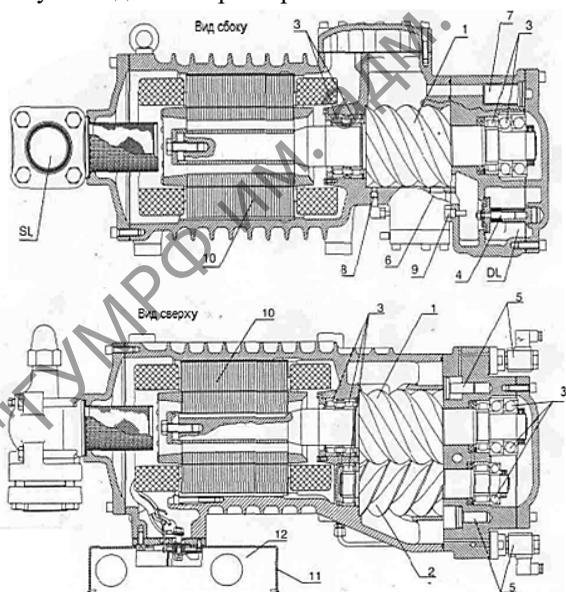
Схема герметичного винтового компрессора Битцер HS:
